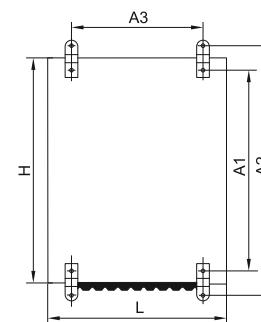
Вид корпуса сзади / Figure 1 – Enclosure back elevation / 1 сурет – Корпуштың артқы көрінісі
